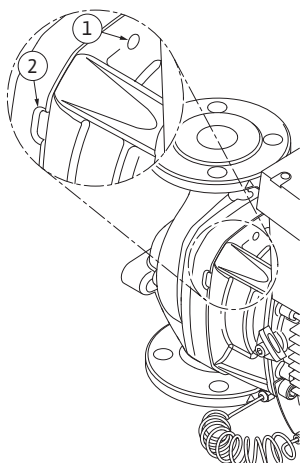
Alezaje filetate și fante pentru împingerea ansamblului motor cu rotor hidraulic din carcasa pompei
